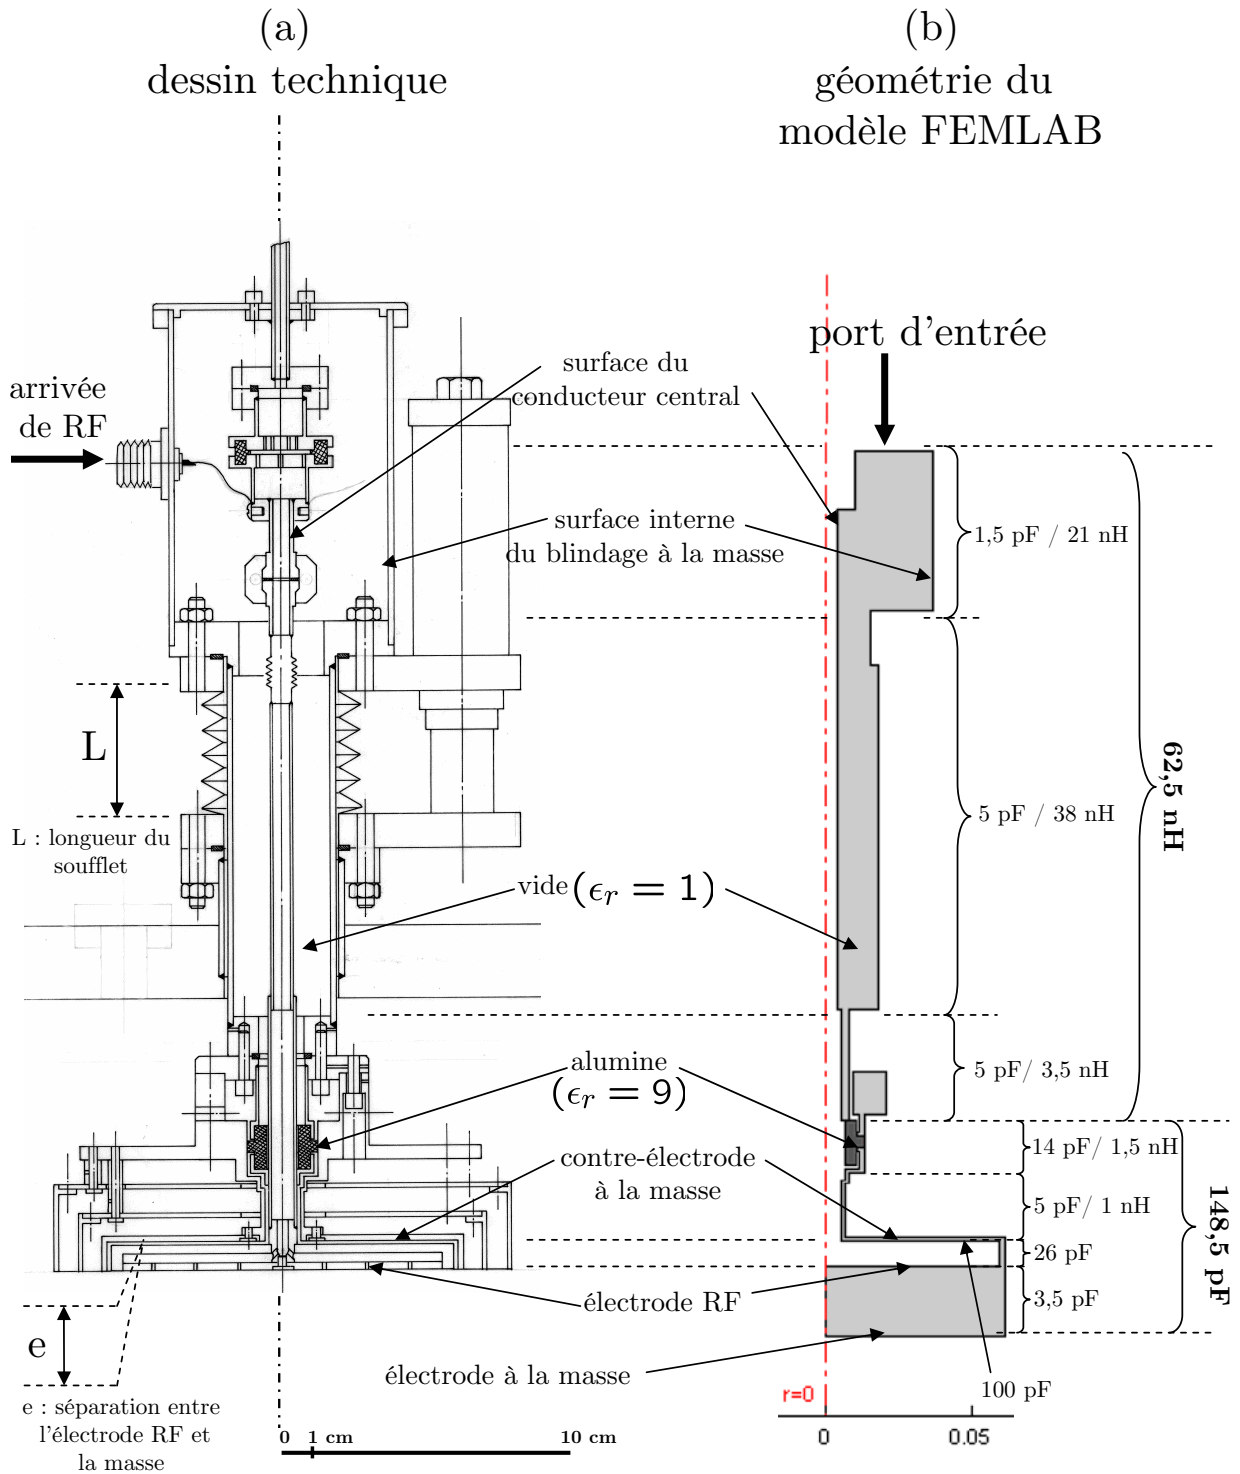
Dessin technique (a) et géométrie du modèle Femlab du réacteur avant modification.
